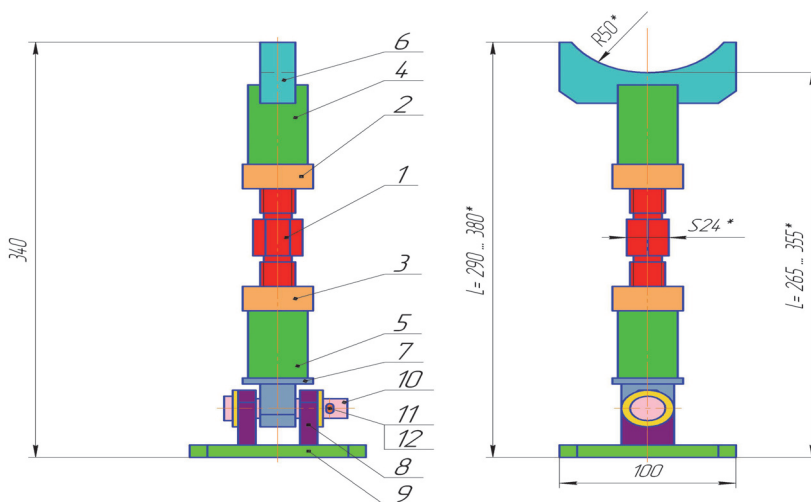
Приспособление для демонтажа поводков тепловоза ТЭ25 (чертеж 448.02.00.000)
